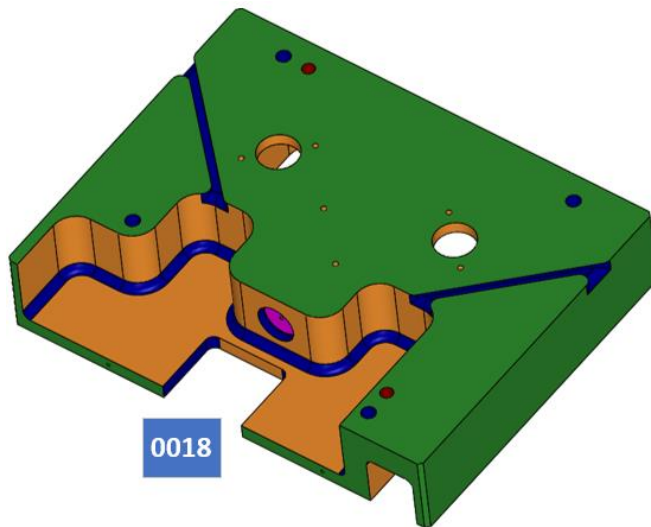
Placa intermédia (Suporte injeção a quente): Vista isométrica
